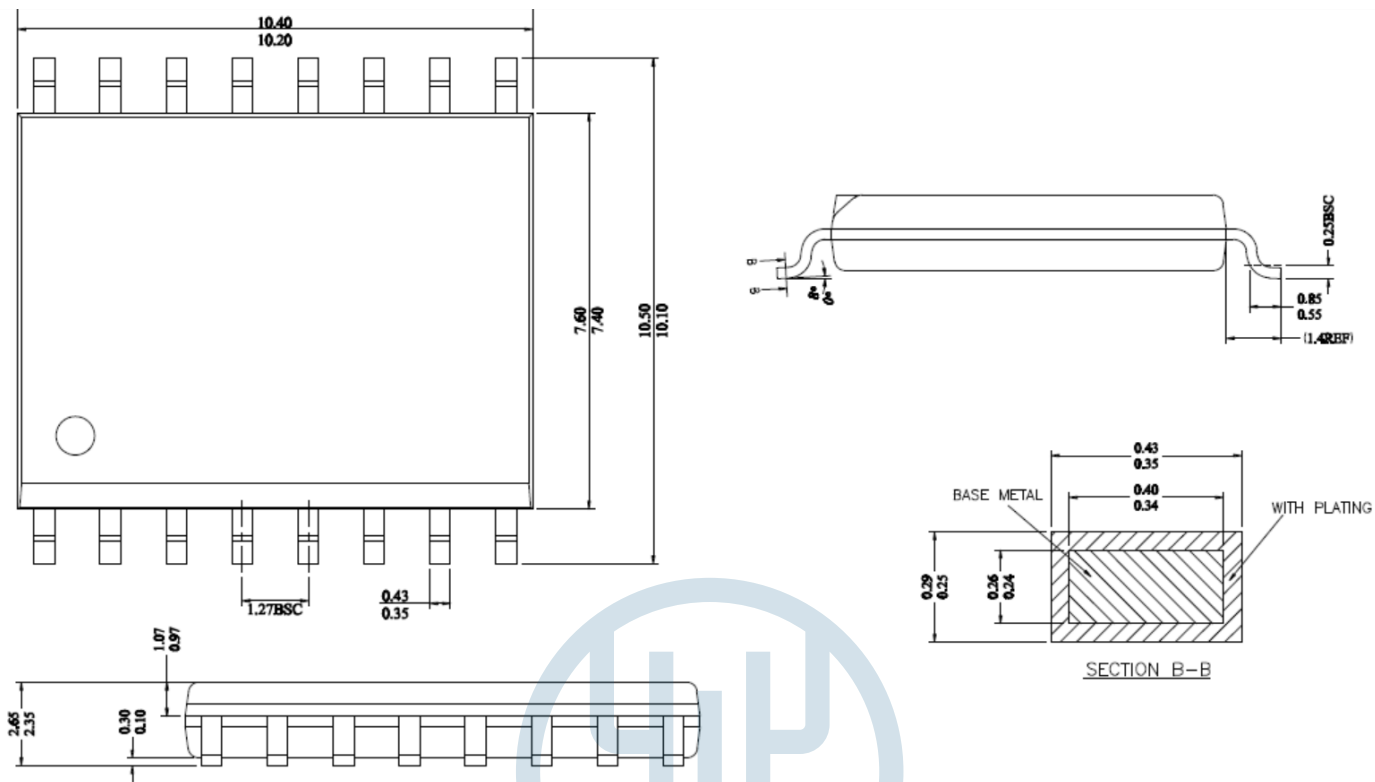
WB SOIC-16 封装外形尺寸-尺寸单位(mm)
